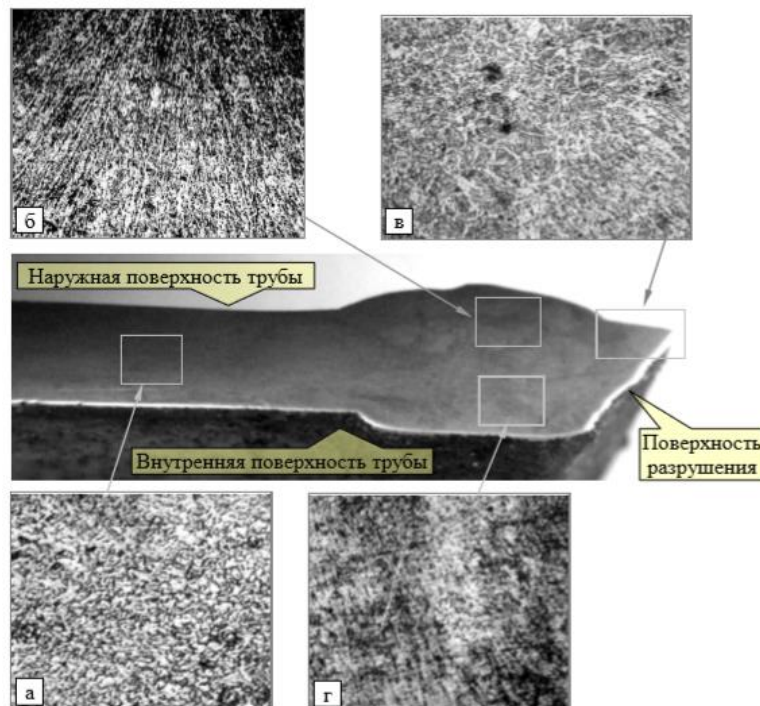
Микроструктура материала трубы и сварного соединения вблизи поверхности разрушения (поперечный шлиф), *5: а - структура основного металла трубы: феррито-перлитная смесь в отожженном состоянии, *50; б, г - сварной шов: б - верхний шов - столбчатая литая структура, *50; г - нижний шов - частично перекристаллизованная литая структура, *50; в - граница сплавления верхнего шва, *50.
